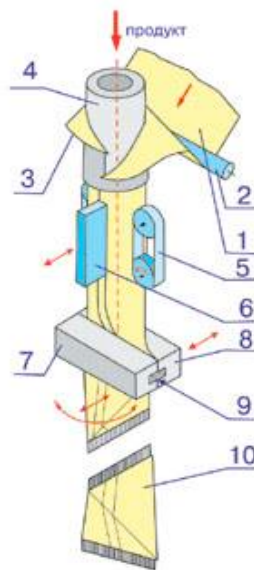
Компонування машини з поворотними зварними губками: 1 – рулон плівки; 2 – натяжний механізм; 3 – формуючий механізм; 4 – рукавотворювач; 5 – механізм протягування плівки; 6 – механізм поздовжнього зварювання; 7, 8 – губки поперечного зварювання; 9 – відрізний ніж; 10 – готовий пакет
